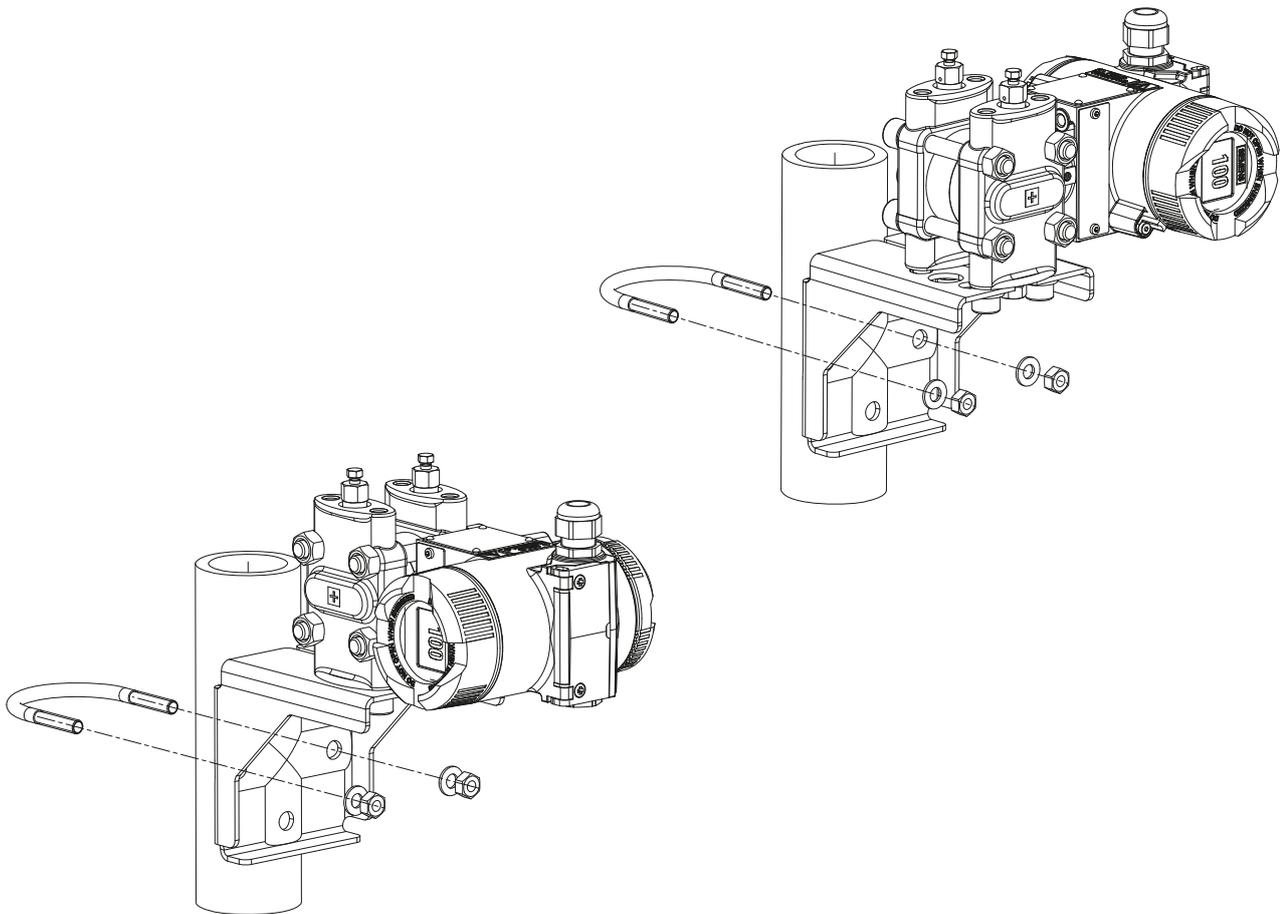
Fixation avec l'équerre de montage à l'exemple de la pression différentielle sur des conduites de pression active verticales
